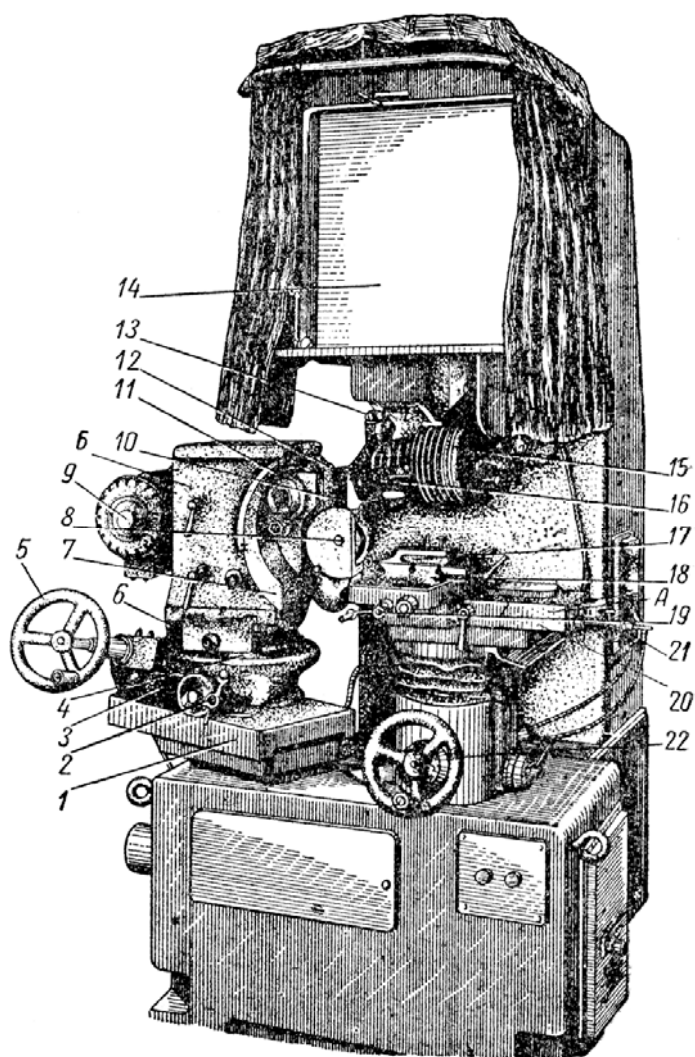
Общий вид профишлифовального станка мод. 395М1
